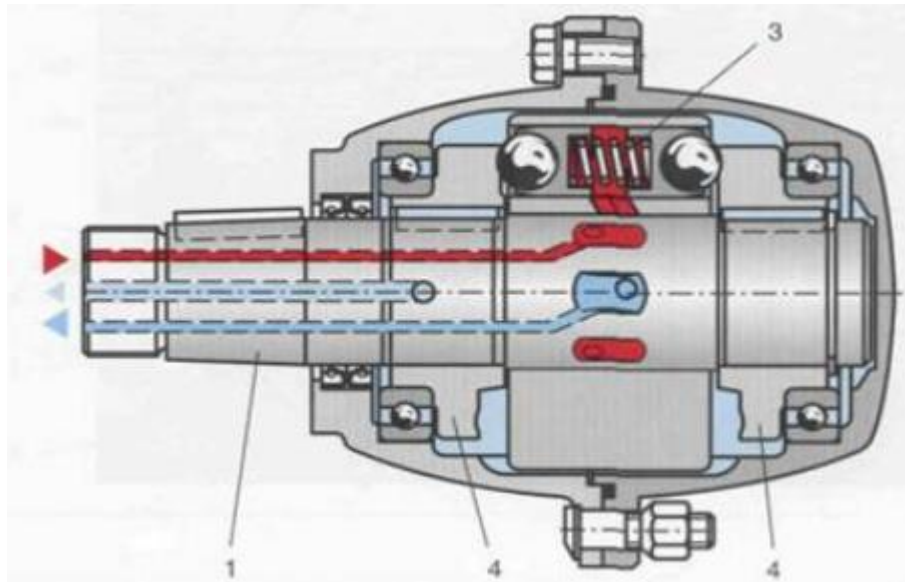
Аксиально-поршневий гідромотор з корпусом, що обертається, і нерухомим валом
